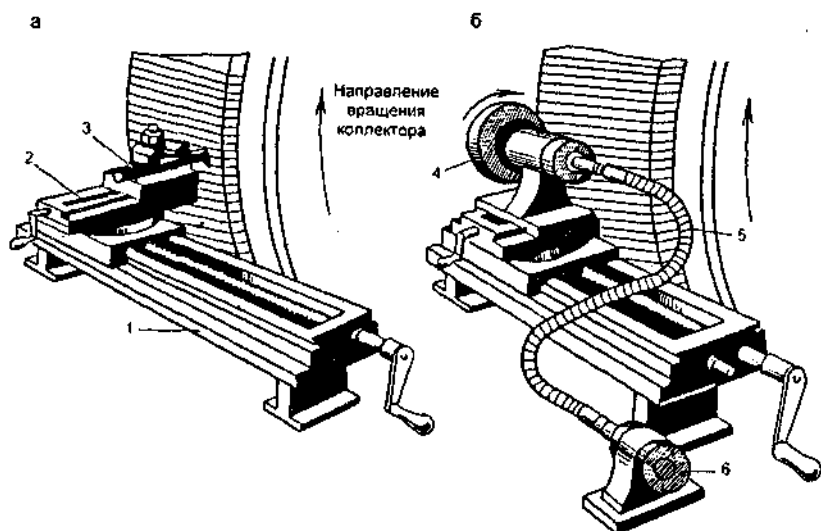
Переносные приспособления для обточки (а) и шлифовки (б) коллектора: 1 – станина; 2 – суппорт; 3 – резец; 4 – карборундовый круг; 5 – гибкий вал; 6 – электродвигатель
